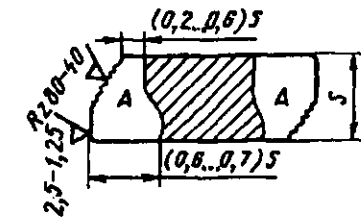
Шероховатость поверхности, достигаемая при отрезке заготовок на ножницах: А — упрочненный металл
